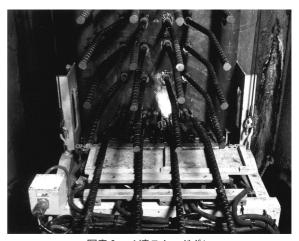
4 連スタッドガン Automatic multi-stud welding machine (NS Stud Gun)
